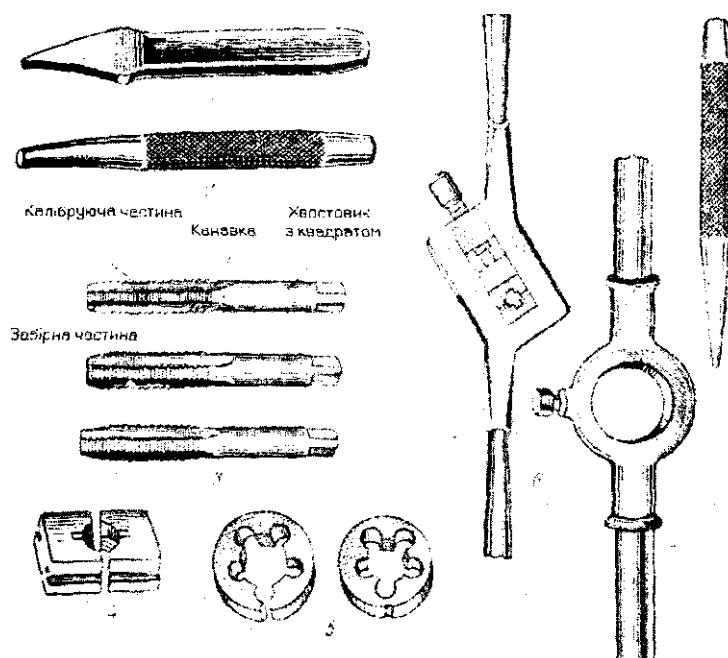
Інструменти для рубання, пробивання отворів і нарізання різьби:
